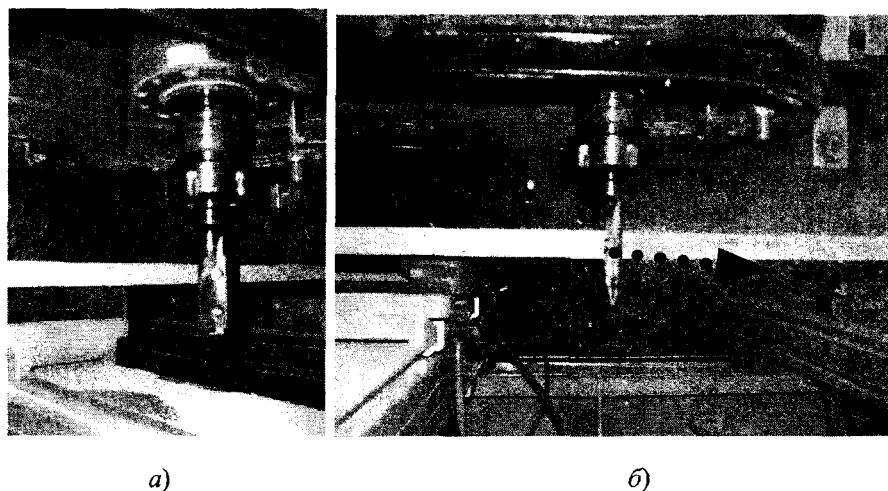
Сборная фреза $\varnothing 20$ мм со сменными твердосплавными ножами, $z = 1$ шт., $\lambda = 0^\circ$, установленная в шпинделе станка (а) и выход стружки и пыли из зоны резания при неполном фрезеровании (б)
